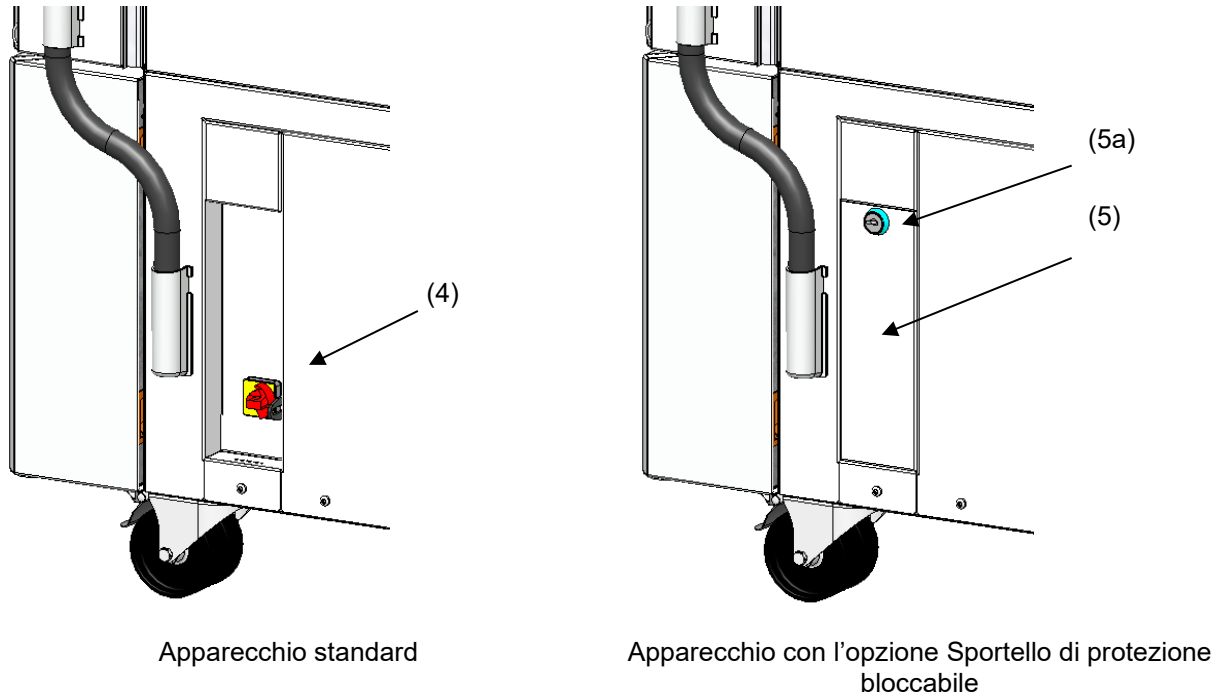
Posizione dell'interruttore generale e lo sportello di protezione bloccabile (opzionale) sul lato destro dell'apparecchio
